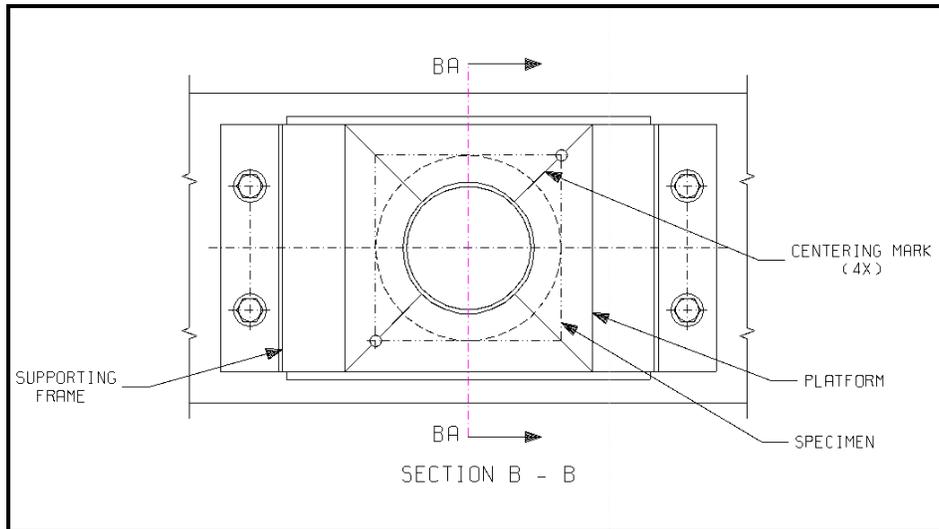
Montage d'essai : Bâti-support et plateforme : Section BB de la figure 15
